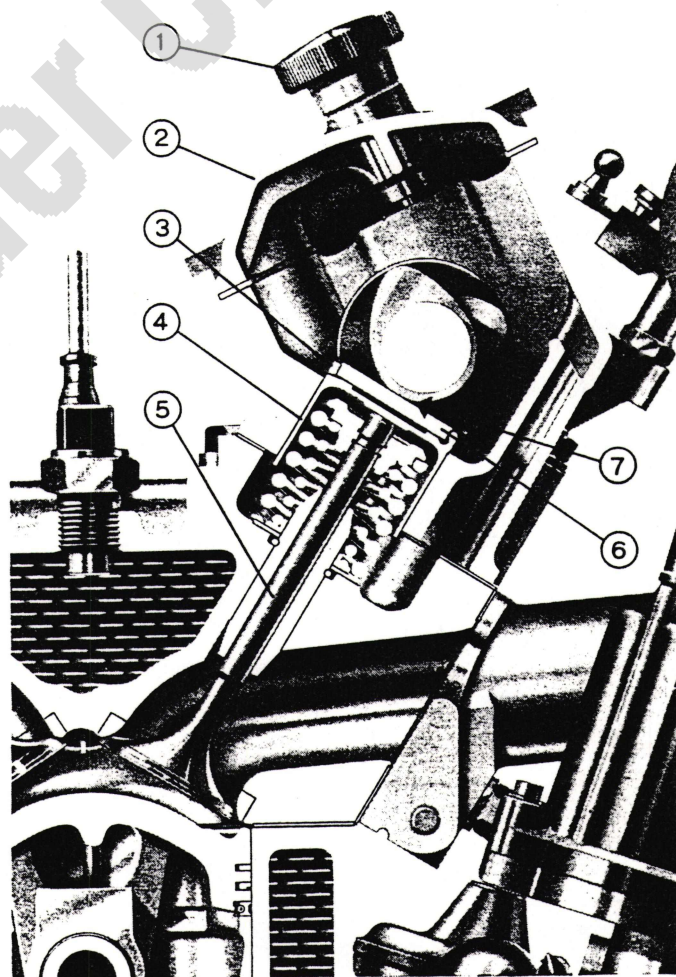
Teilansicht des Motorsquerschnitts am Einlassventil.
